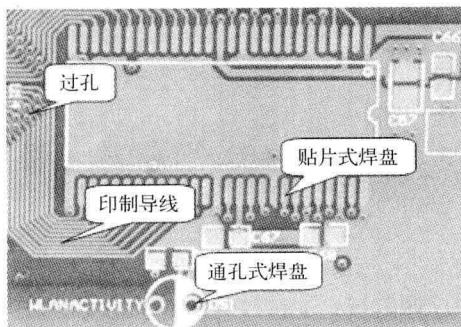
PCB 上的印制导线、过孔和焊盘
